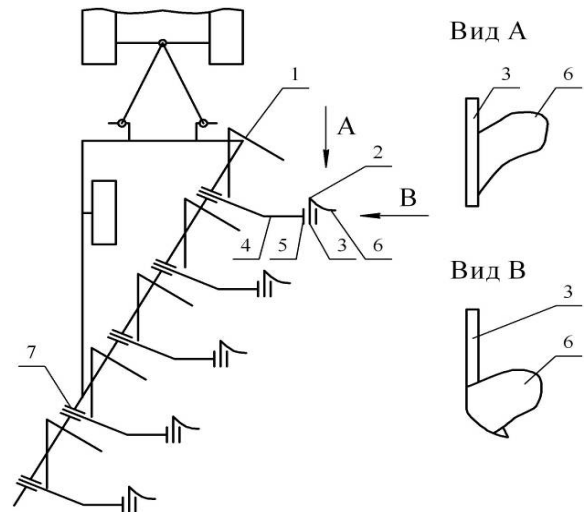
Схема борозноутворювача і його установки на плуг
